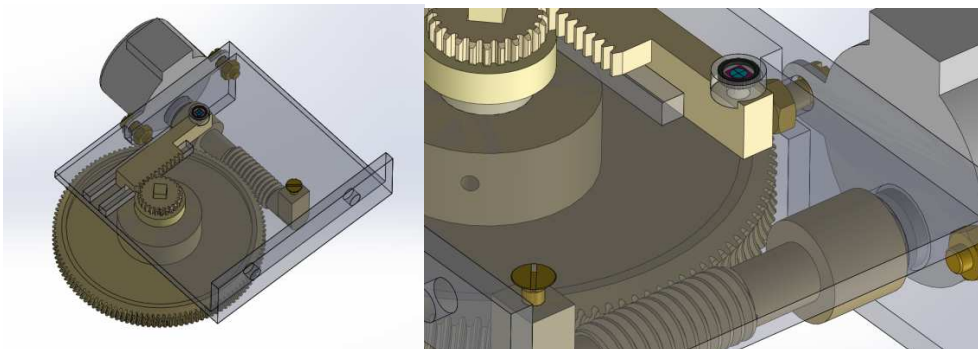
Diseño del mecanismo posicionador para el detector segmentado
